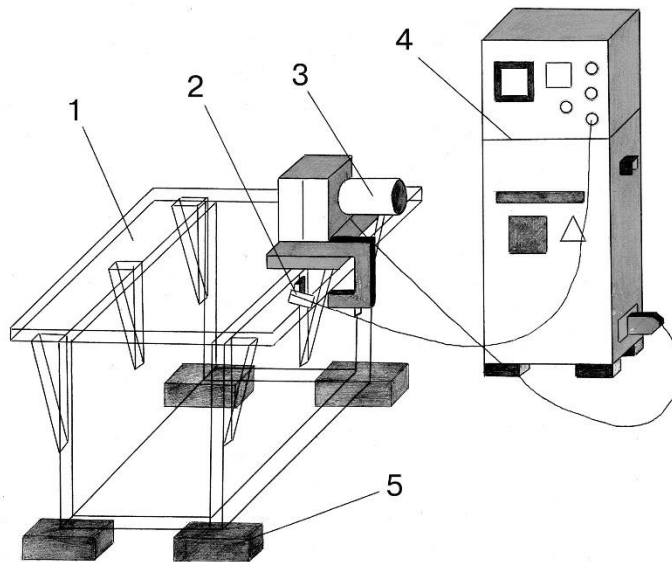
Схема вибрационной обработки сварных конструкций [14]
